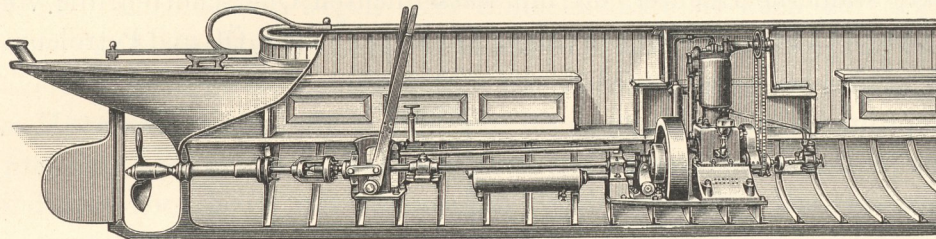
Maschinenanlage mit Otto-Motor und Meißners Umsteuerschraube.
